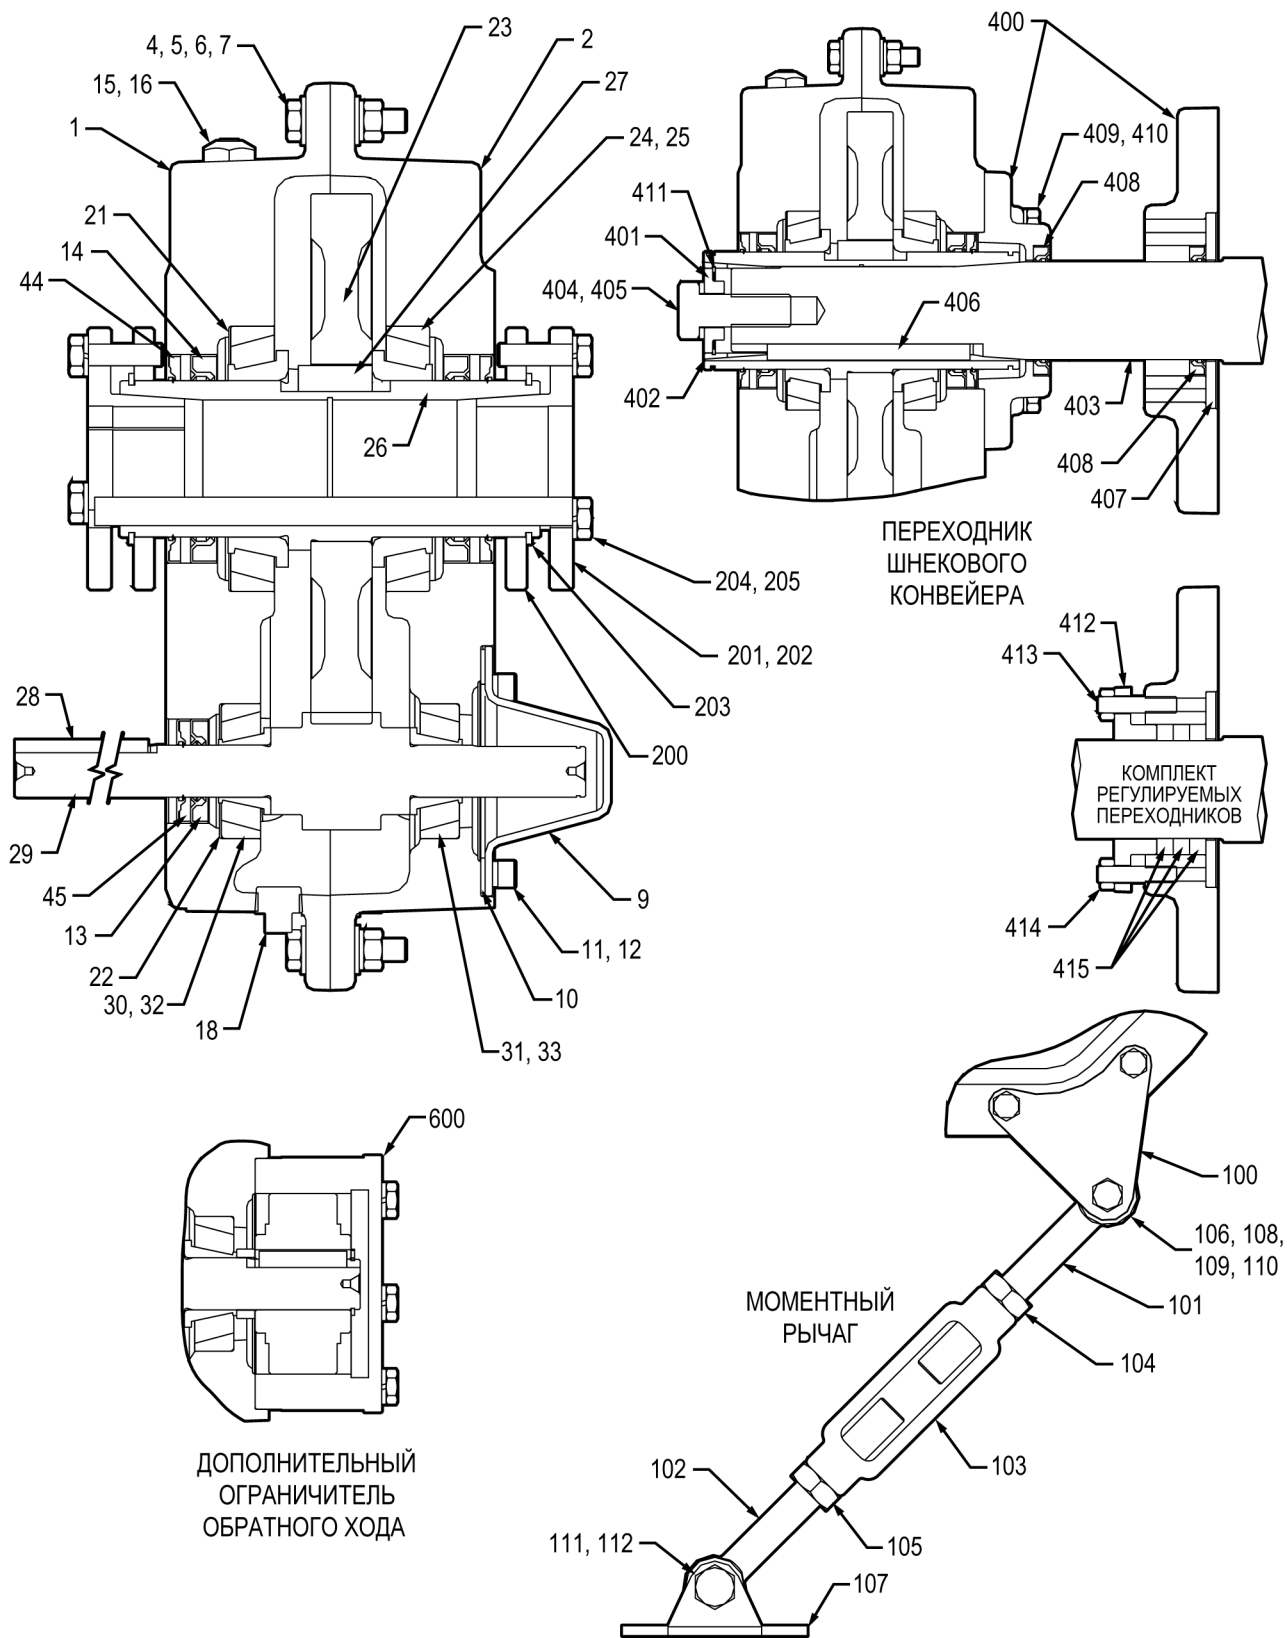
Детали для одноступенчатых редукторов с коническими втулками ТА0107L-ТА7315Н
